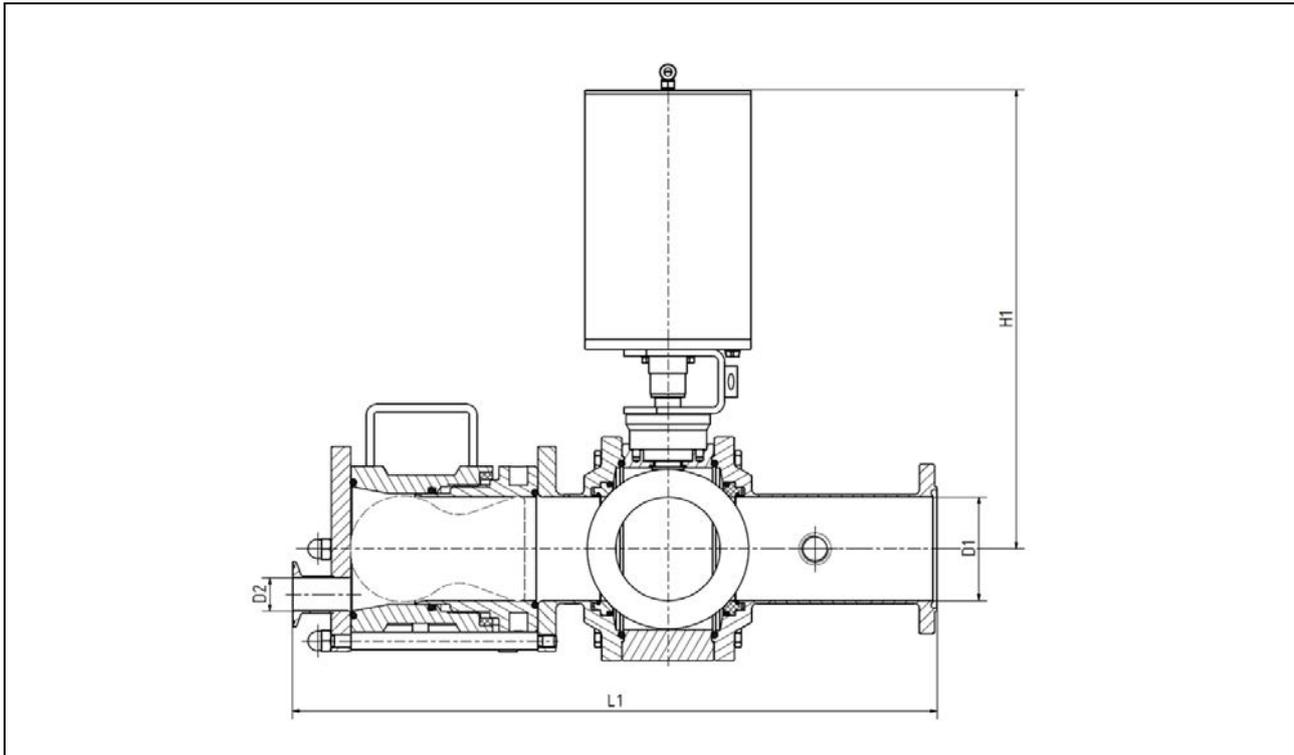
Steckkammer mit Kugelventil, Anschlussvariante Zoll, Serie D
